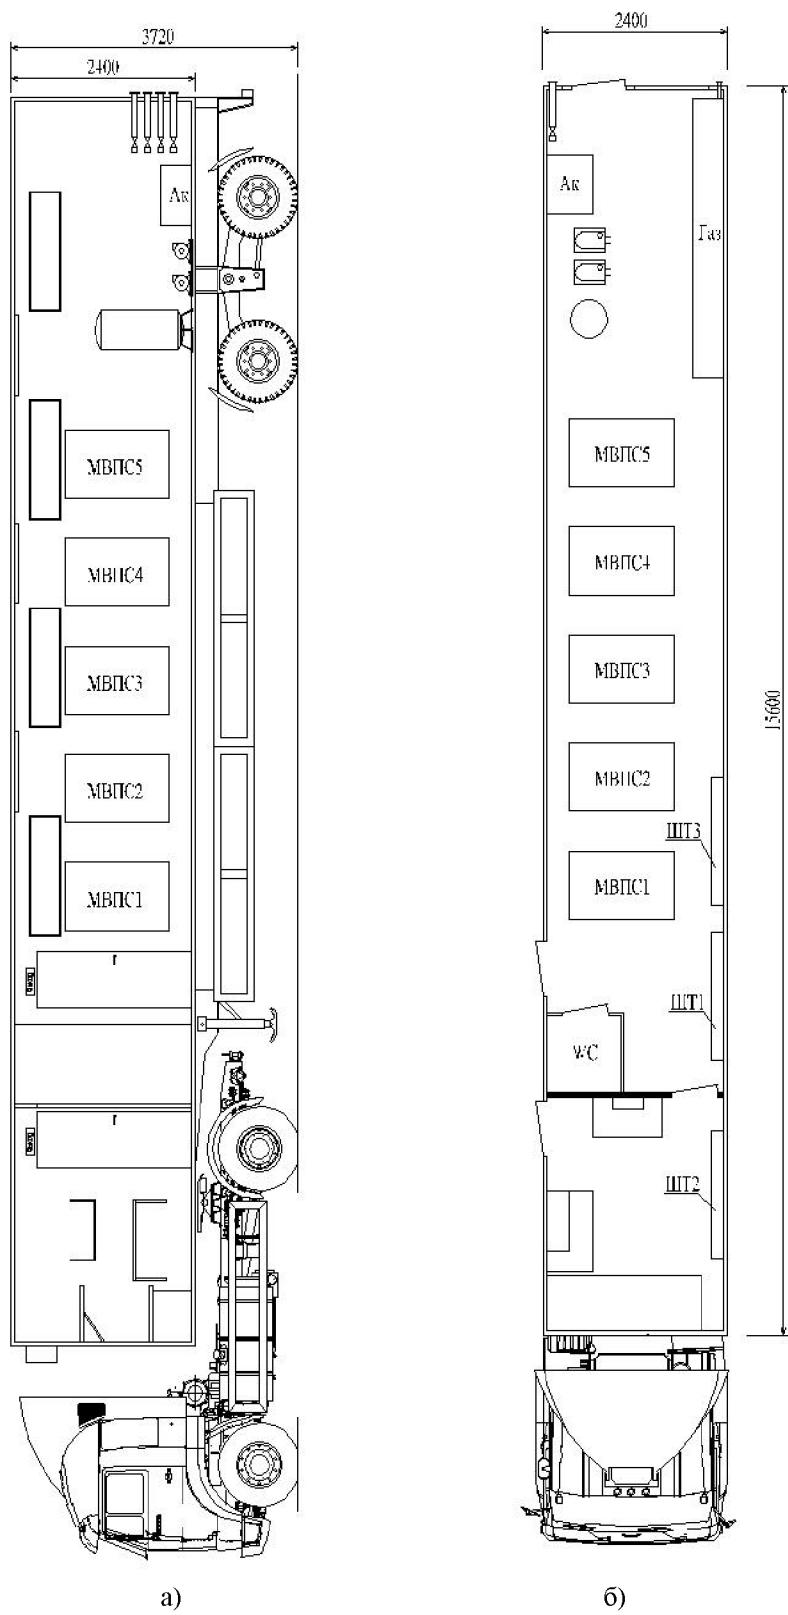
КАМАЗ (а – вид сбоку; б – вид сверху)
